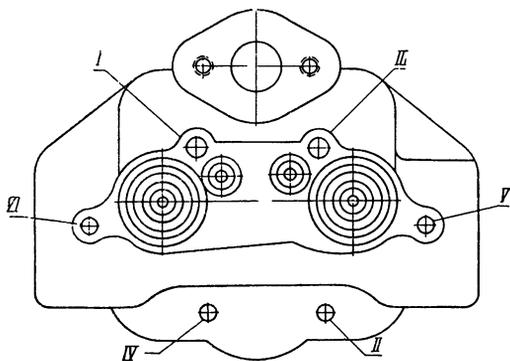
Порядок затягивания болтов крепления головки цилиндров.
